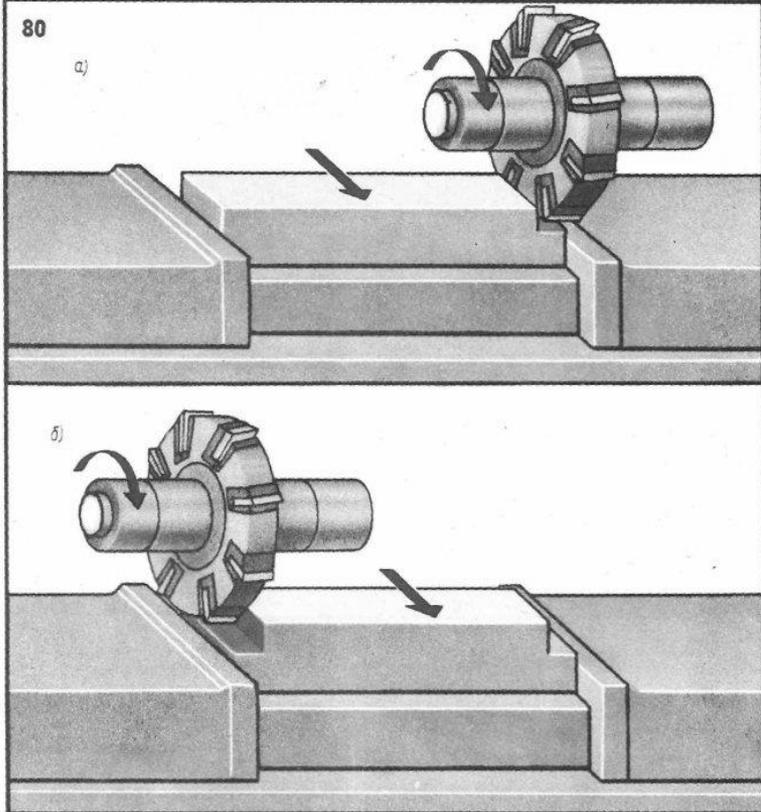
Схема фрезерования уступа дисковой фрезой на горизонтально-фрезерном станке.
